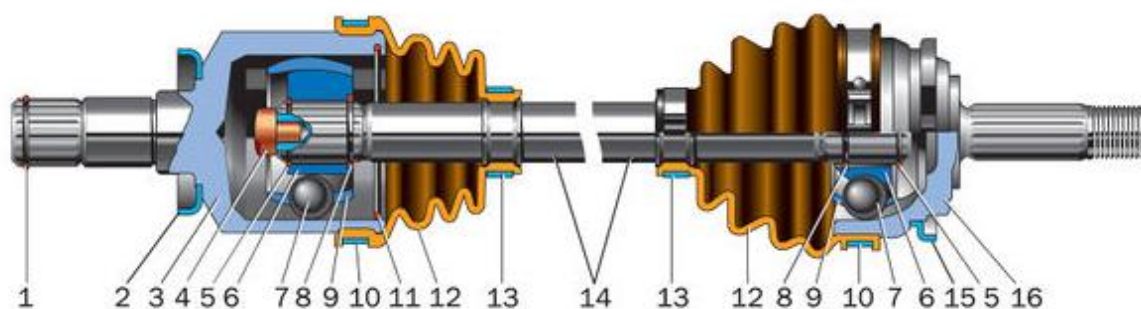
Универсальный шестишариковый карданный шарнир типа “ГКН”: 1 – стопорное кольцо корпуса внутреннего шарнира; 2 – защитное кольцо внутреннего шарнира; 3 – корпус внутреннего шарнира; 4 – упор вала; 5 – стопорное кольцо; 6 – обойма; 7 – шарик; 8 – упорное кольцо; 9 – сепаратор; 10 – наружный хомут; 11 – фиксатор внутреннего шарнира; 12 – защитный чехол; 13 – внутренний хомут; 14 – вал привода колёс; 15 – защитное кольцо наружного шарнира; 16 – корпус наружного шарнира
